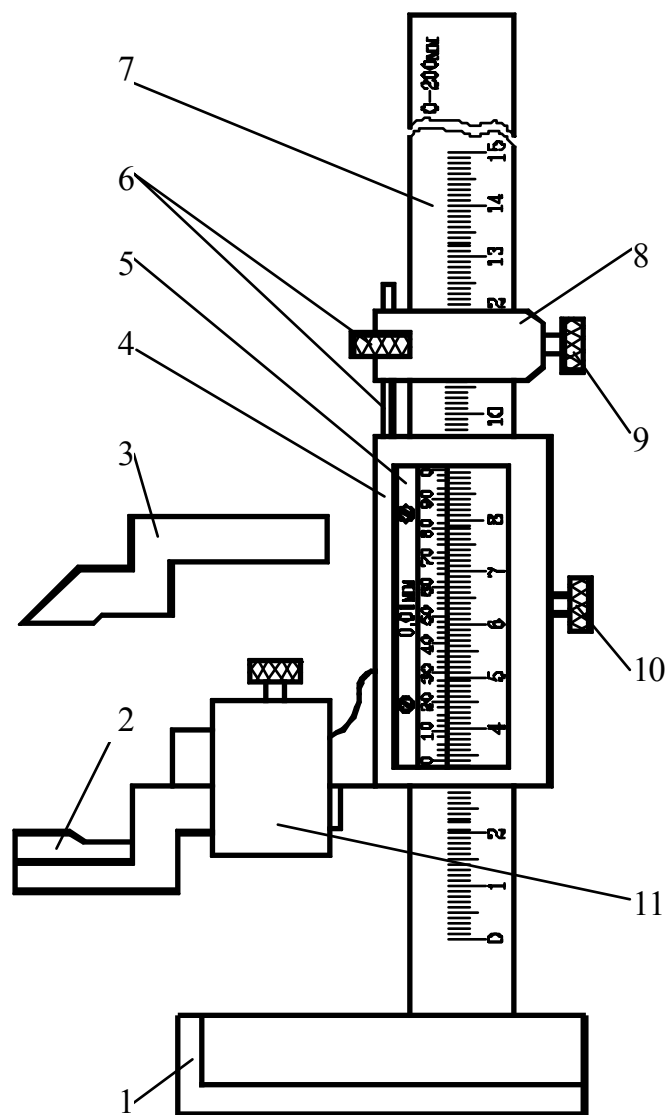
Штангенрейсмас: 1 – основание; 2 – измерительная ножка; 3 – разметочная ножка; 4 – рамка; 5 – нониус; 6 – винт и гайка микрометрической подачи; 7 – штанга; 8 – рамка микрометрической подачи; 9 – зажим рамки микрометрической подачи; 10 – зажим рамки; 11 – хомут
